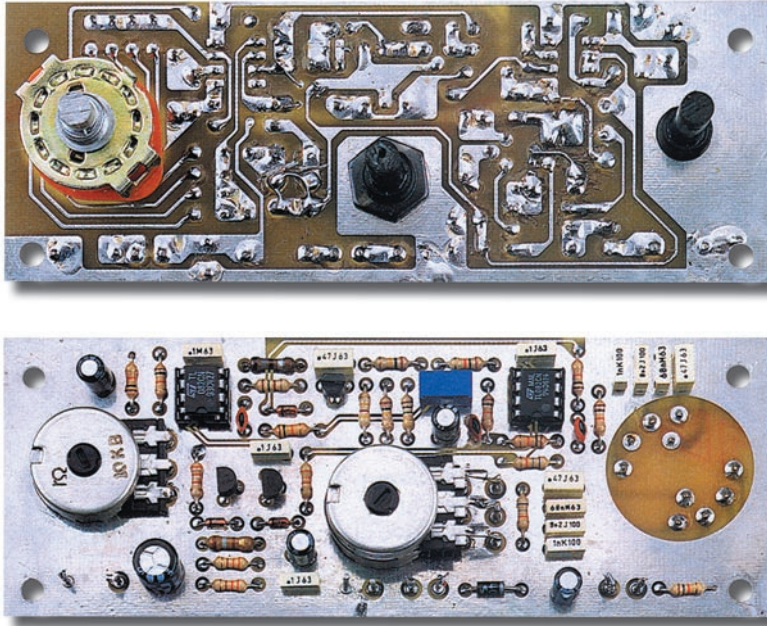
Photo du circuit imprimé double face à trous métallisés du générateur d'ondes sinusoïdales. En haut, vue du côté soudures : S1 est soudé de ce côté. En dessous, vue du côté composants : les potentiomètres seront fixés sur cette face.
